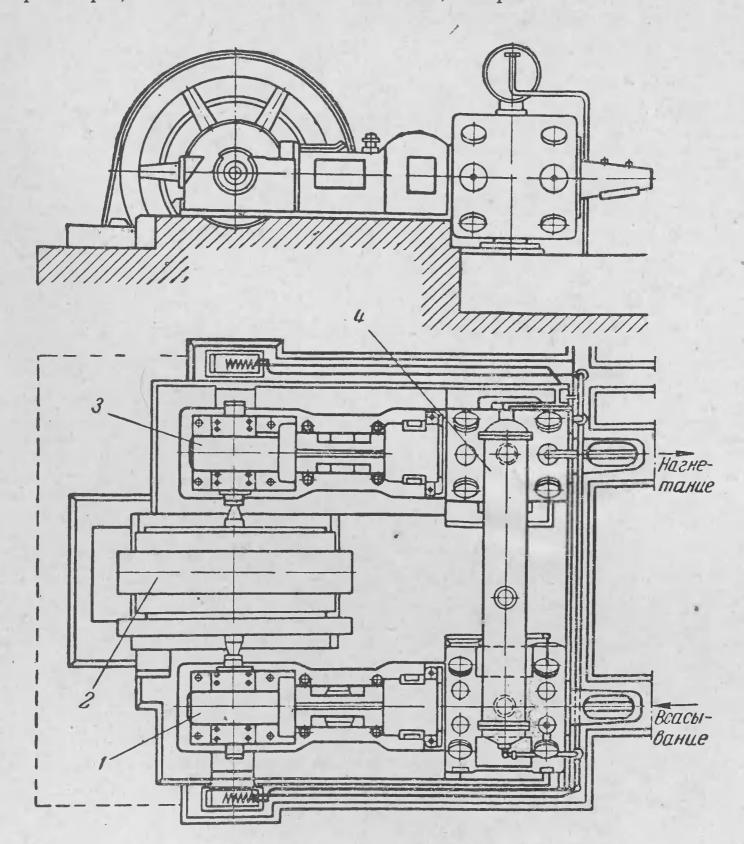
Компрессор 55В (воздушный, ход поршня 55 см). 1— цилиндр первой ступени; 2— электродвигатель; 3— цилиндр второй ступени; 4— промежуточный холодильник.
